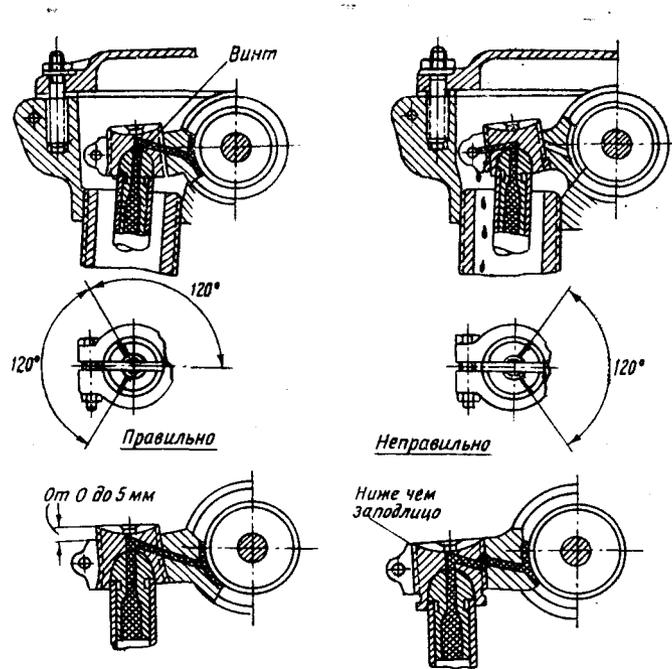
Установка регулировочного винта в рычаге клапана и предельные положения регулировочного винта
